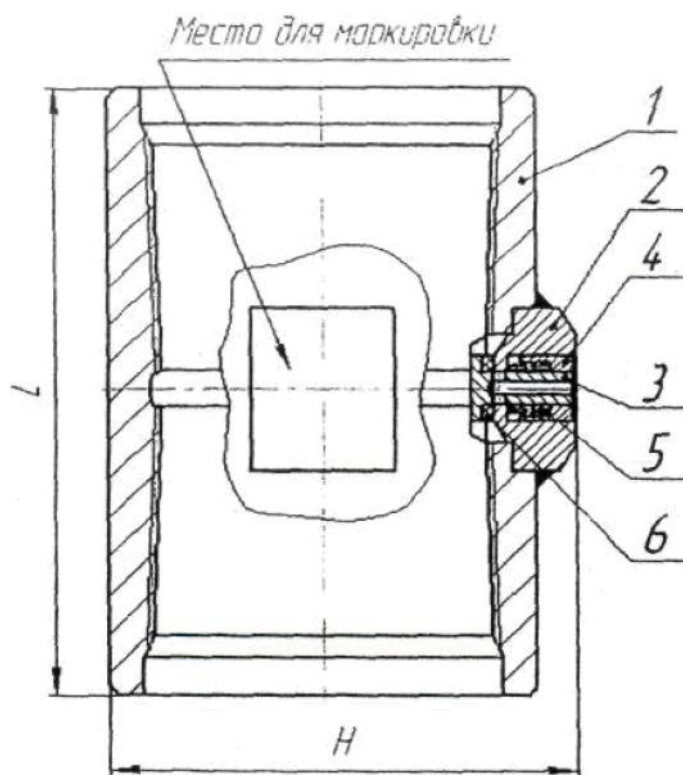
Общий вид клапана: 1 – корпус (муфта); 2 – корпус; 3 – золотник; 4 – гайка; 5 – пружина; 6 – прокладка уплотнительная.
